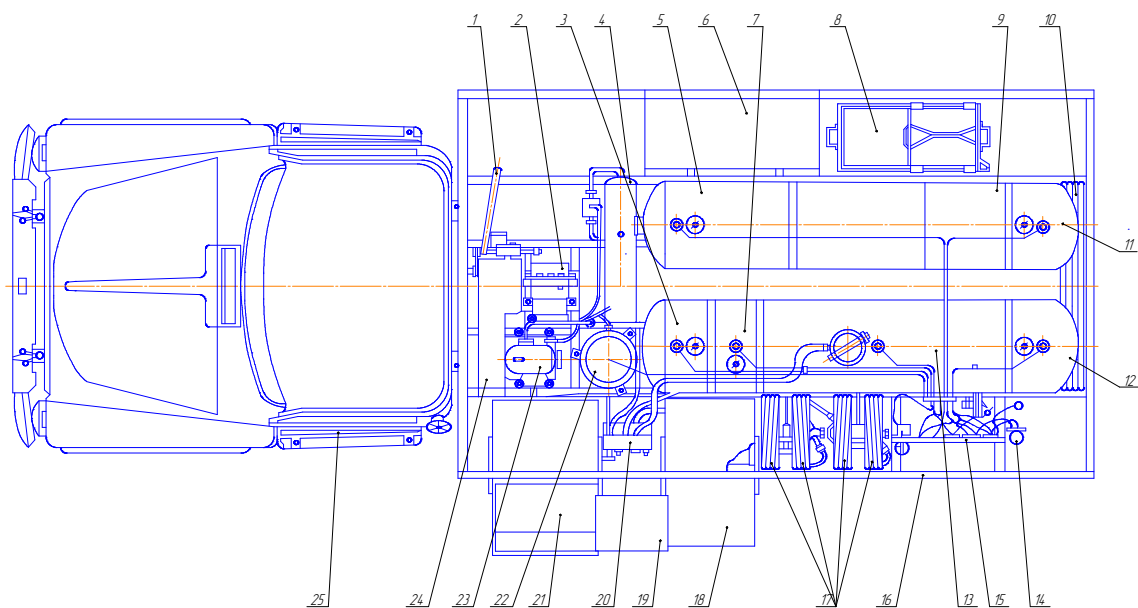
Схема предлагаемой автомастерской на базе шасси ЗИЛ-130
